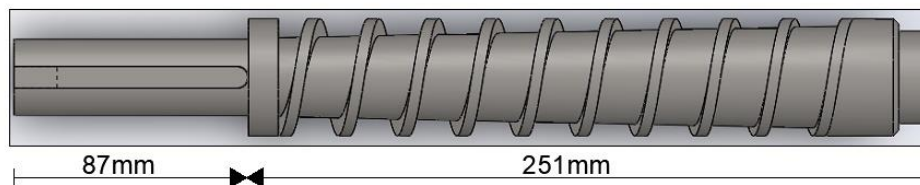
Dimensiones del tornillo extrusor. Fuente: Autor
